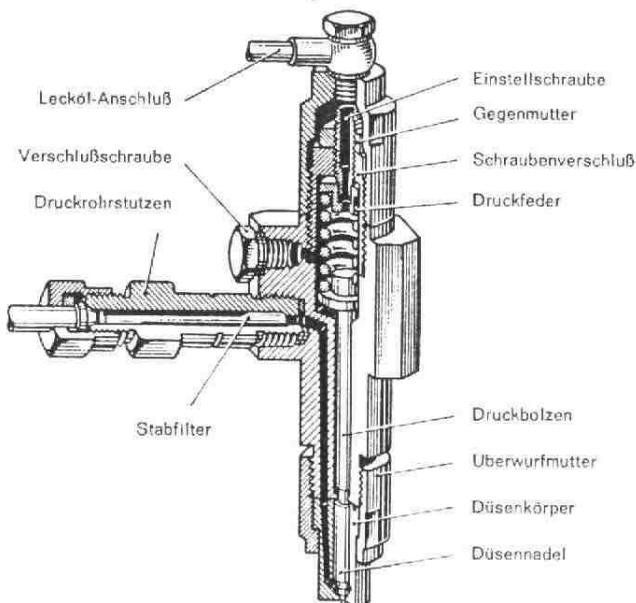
BOSCH-Düsenhalter mit eingebauter Düse
